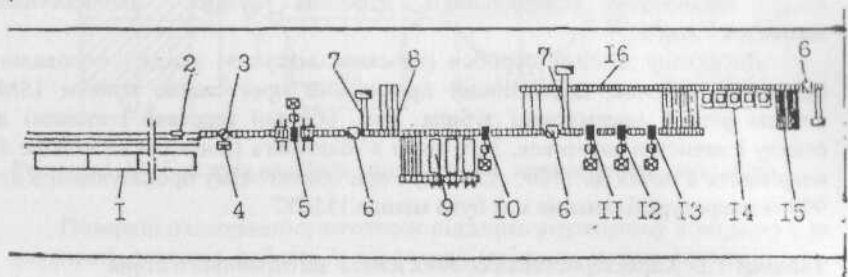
Блюмінг 1150 і трубозаготовочний стан 900/750: 1 - нагрівальні колодязі; 2 - слитковіз; 3 - поворотний пристрій; 4 - перекидач; 5 - робоча кліть 1150; 6 - ножиці; 7 - конвейер прибирання обрізків; 8 - прибиральний пристрій; 9 - методичні печі; 10 - обтискна кліть; 11,12,13 - робочі кліті 750; 14 - пили гарячого різання; 15 - холодильник; 16 - обвідний рольганг
